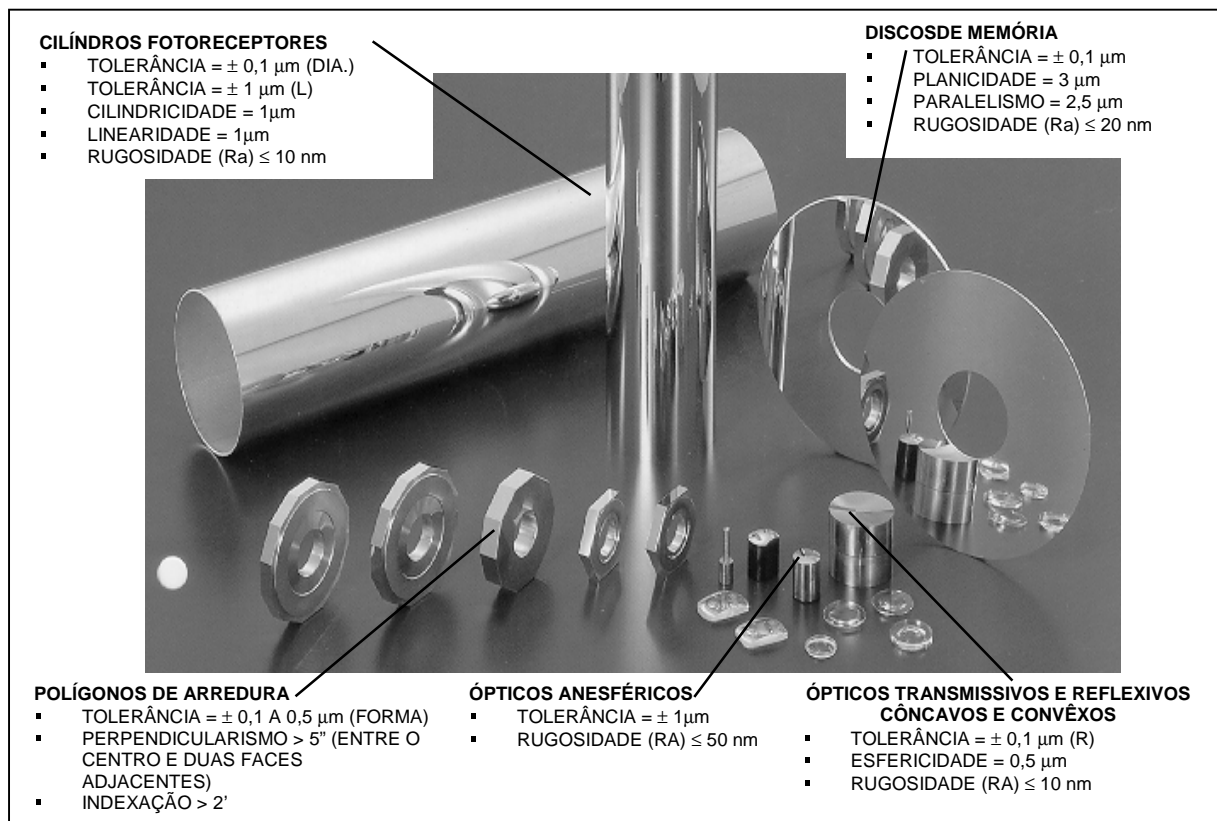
Componentes fabricados por usinagem de ultraprecisão
